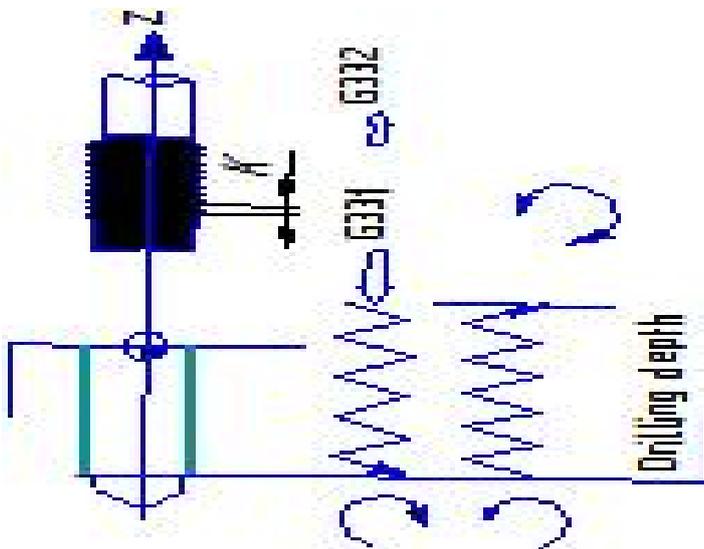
Схема нарезания резьбы метчиком на фрезерном станке с ЧПУ
